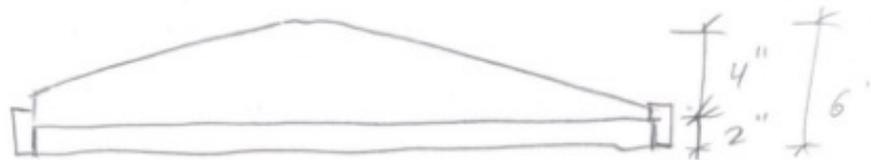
Dessin gabarit usinage : Prototype 2
